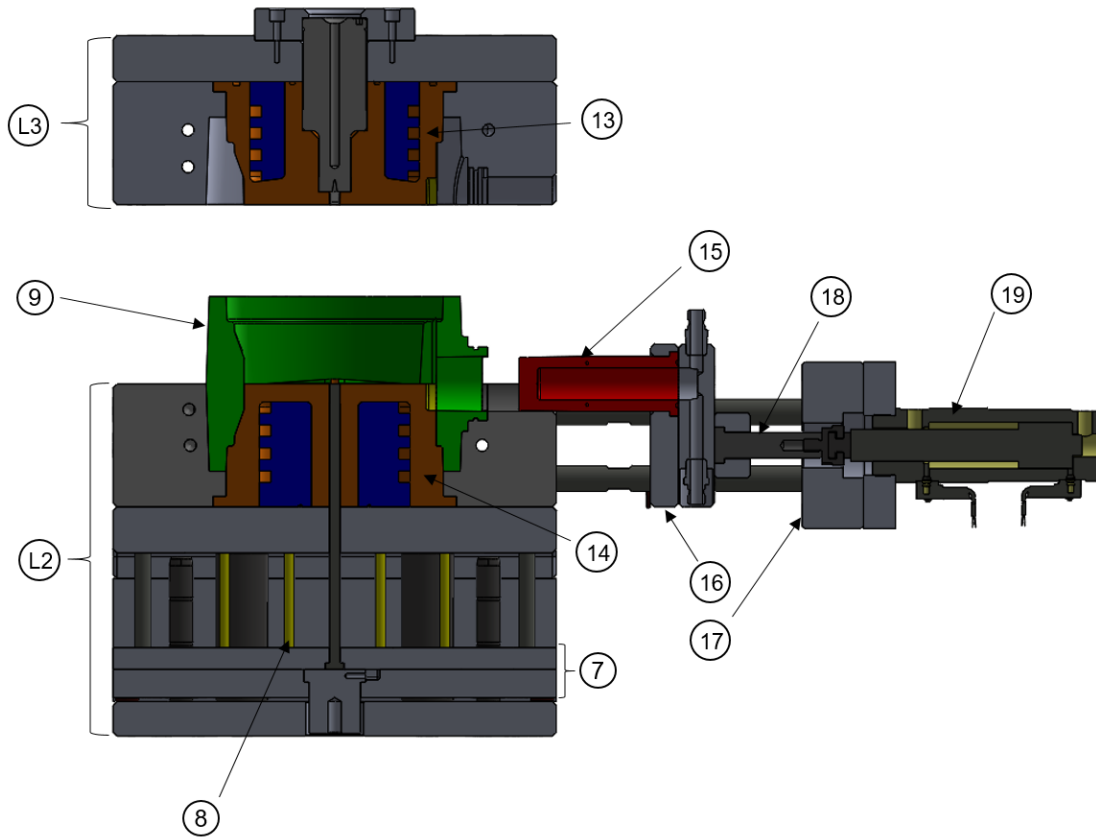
Vista Sección Molde Servo Actuado, Molde Abierto
